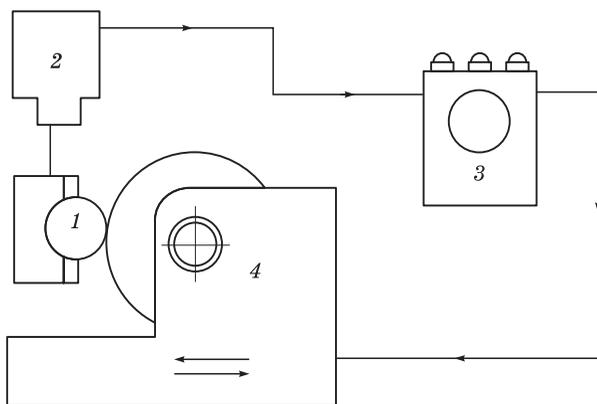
Схема активного контрольно-сортировочного устройства
